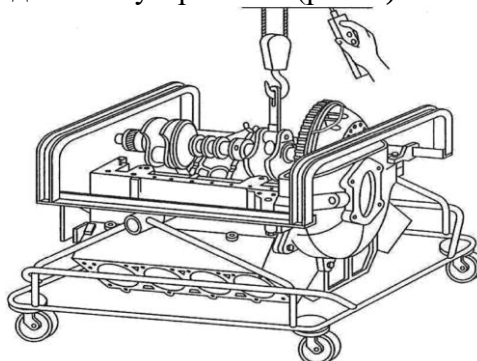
Демонтаж коленчатого вала тракторного двигателя
